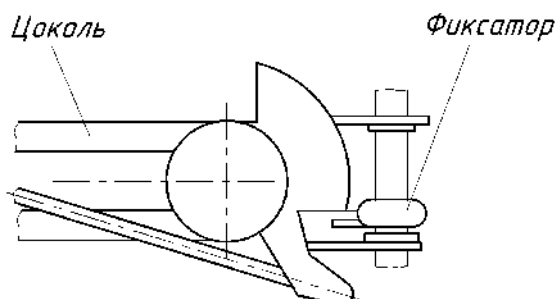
Конструкция механической блокировки разъединителя РДЗ-110
